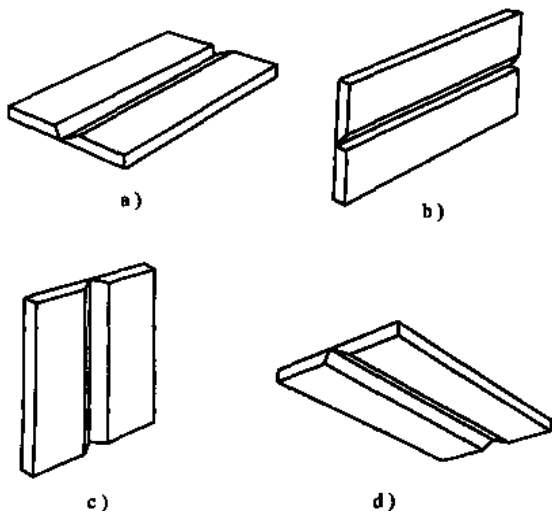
开坡口对接焊缝试板的焊接位置
